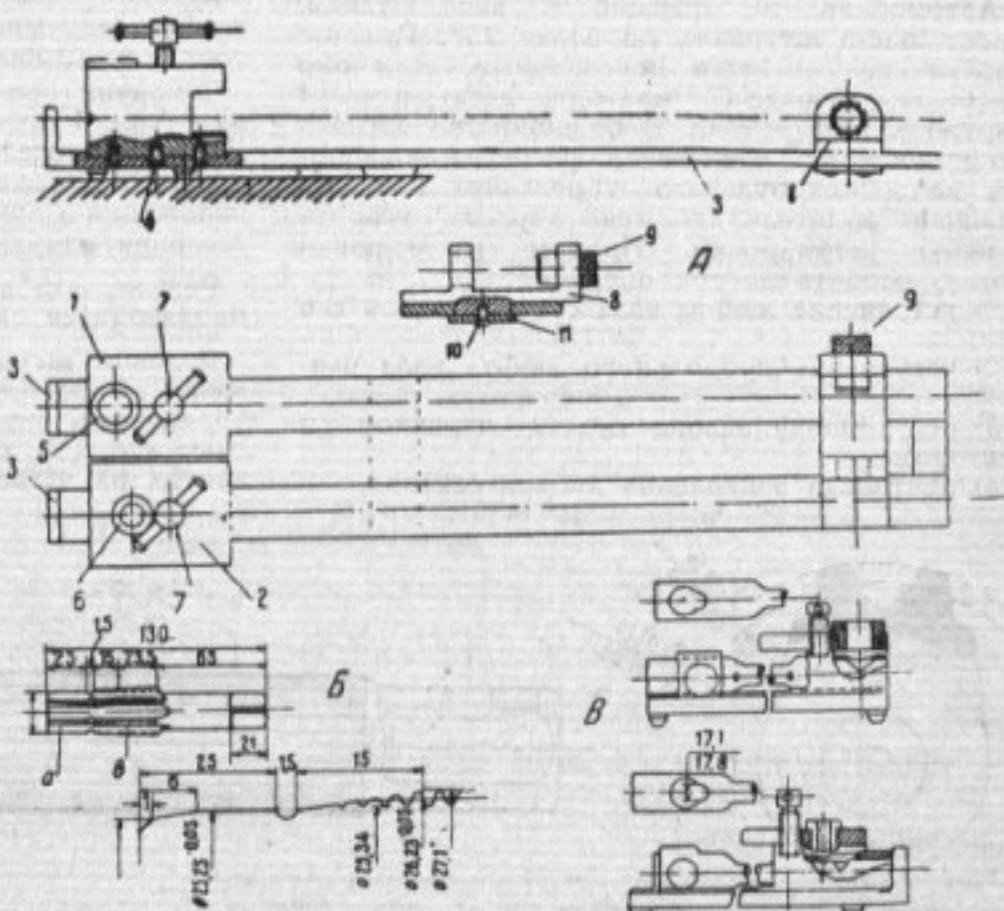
Приспособление для механической обработки тяг рулевого управления ГАЗ-АА
